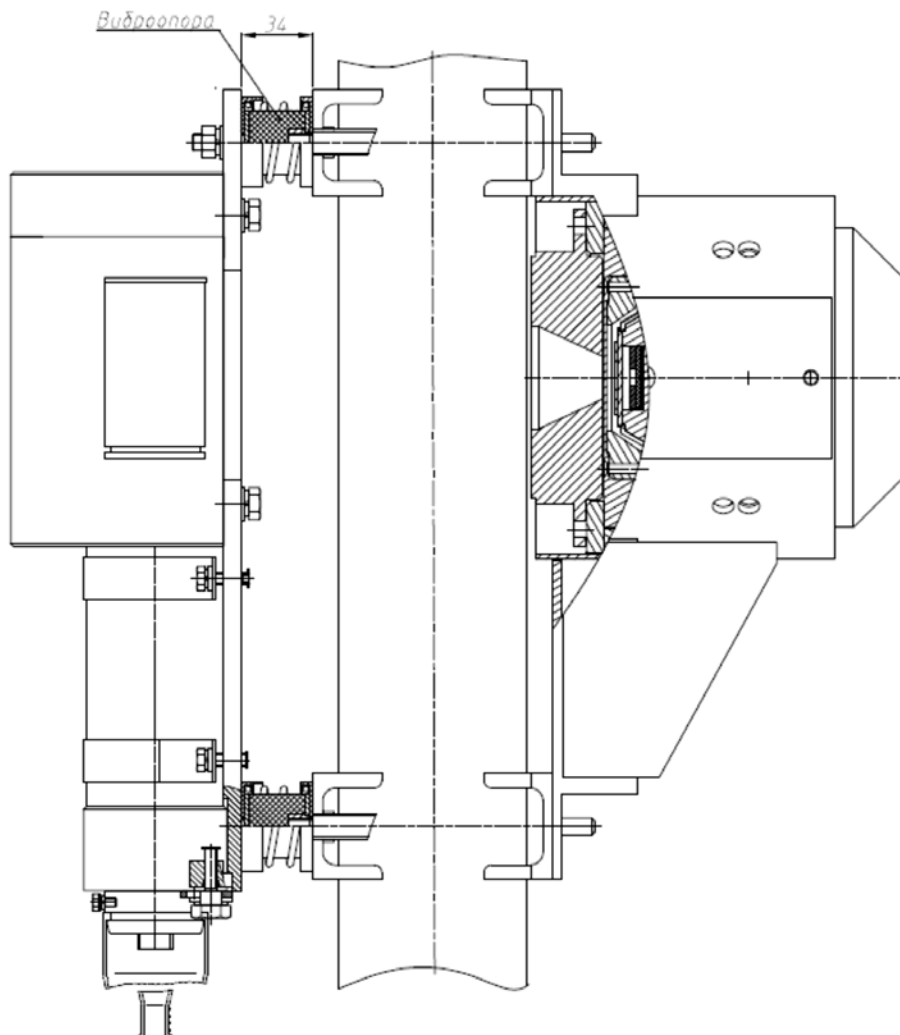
Плотномер с устройством крепления на виброопорах.
